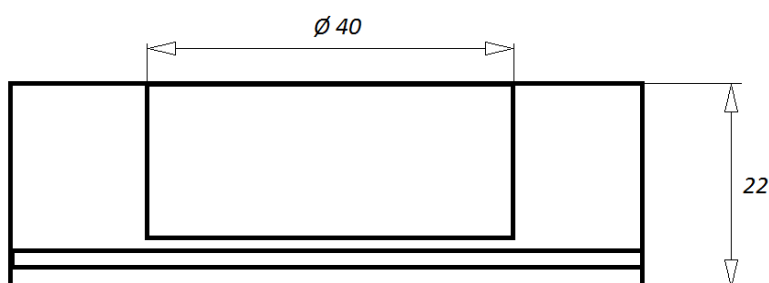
Схема образца для испытаний с цилиндрической полостью
